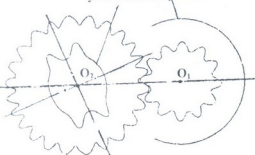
Цилиндрическая зубчатая передача с переменным делительным шагом
